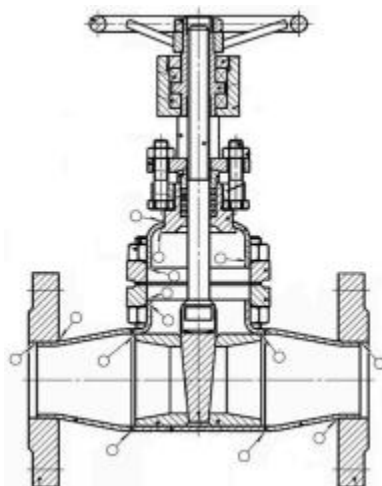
Общий вид задвижки клиновой сварной, предложенной С. А. Курмаевым, Е. Н. Индюшным и Е. С. Шаньгиным [15]
